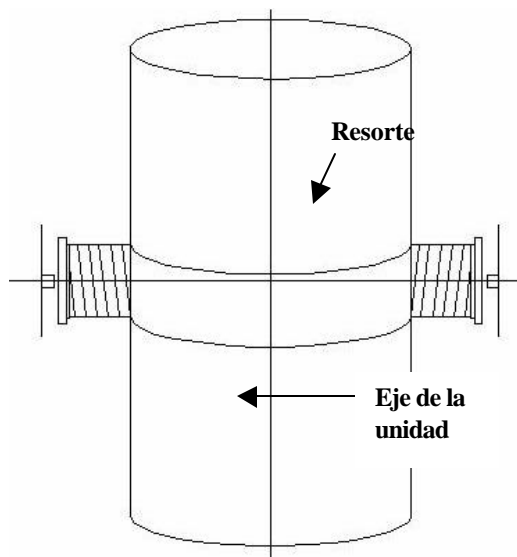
Sensor mecánico de Sobrevelocidad.
